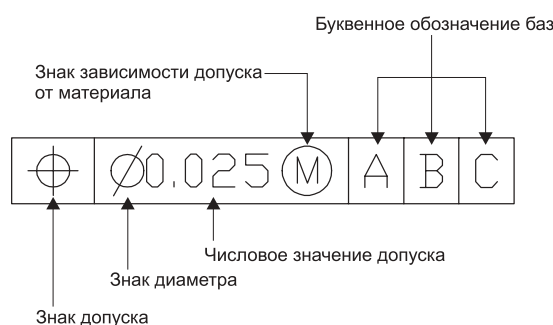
Типовое обозначение допуска отверстия
